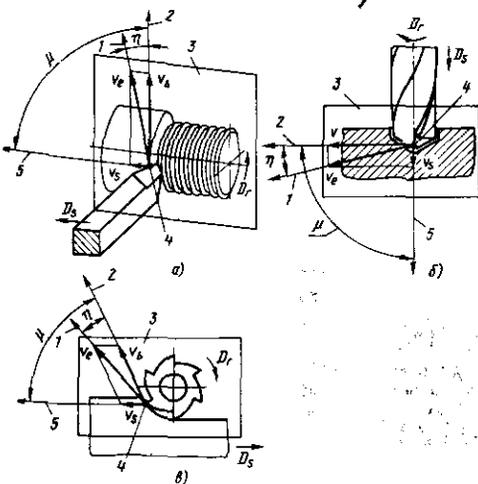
Элементы движений в процессе резания при обтачивании (а), сверлении (б) и фрезеровании (в): 1 — направление скорости результирующего движения резания; 2 — направление скорости главного движения резания; 3 — рабочая плоскость; 4 — рассматриваемая точка режущей кромки; 5 — направление скорости движения подачи
